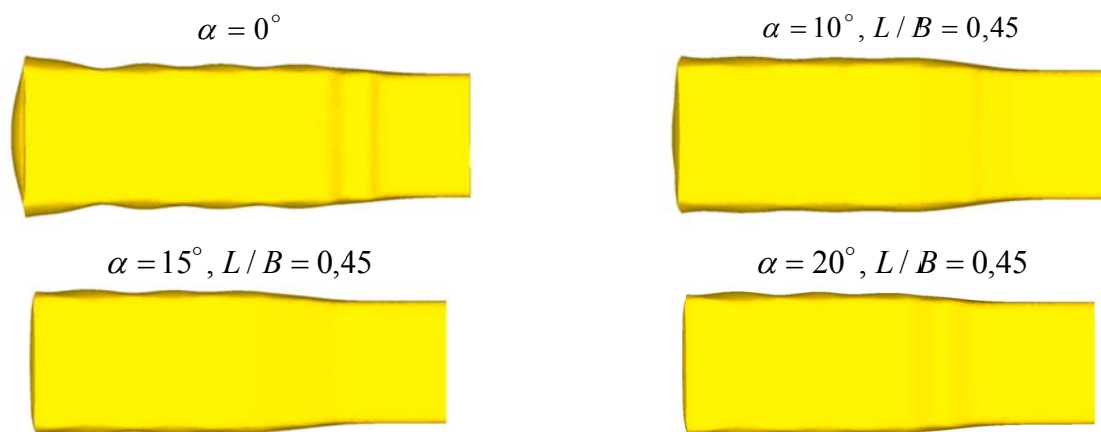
Внешний вид заготовки после протяжки бойками различных размеров (вид сверху) при суммарном относительном обжатии заготовки равном 0,3 (два прохода) и подаче равной 2/3 ширины бойка
